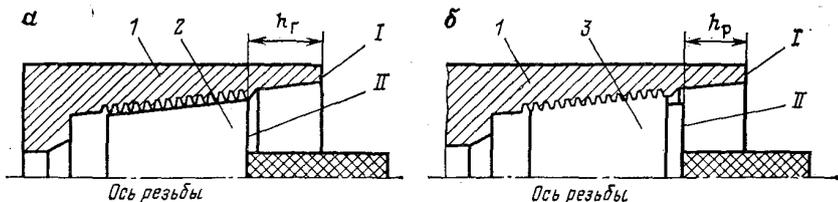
Схема проверки трубной резьбы ТТ замков ЗУК и ЗШК по ГОСТ 5286—75 гладкими и резьбовыми калибр-пробками:
